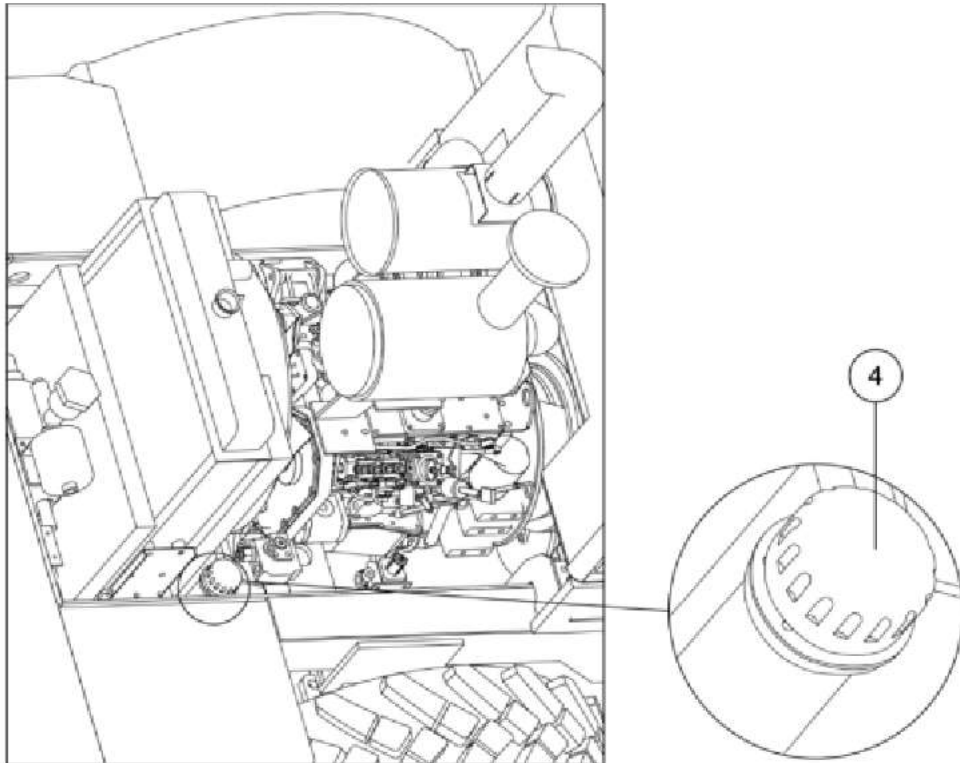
Pokrywa elementu filtra oleju hydraulicznego
